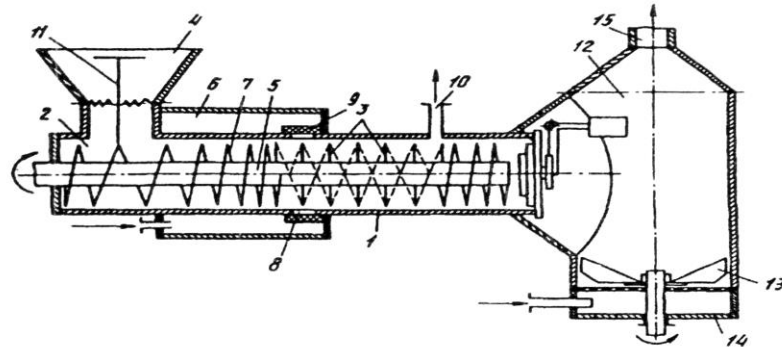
Гвинтовий живильник для нагнітальної пневмотранспортної установки: 1 - корпус; 2 - приймальна камера; 3 - лопатки; 4 - бункер; 5 - шнек; 6 - повітряна камера; 7 - витки ущільнюючої ділянки; 8 - отвори; 9 - кільце; 10 - патрубок; 11 - вібророзпушувач; 12 - камера змішувача; 13 - крильчатка; 14 - днище; 15 - напірний трубопровід
